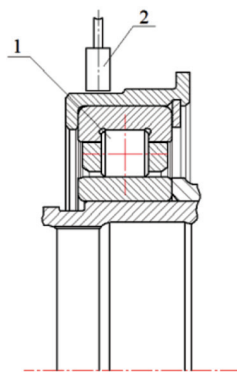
ВОД измеряющий вибрацию корпуса подшипника:
